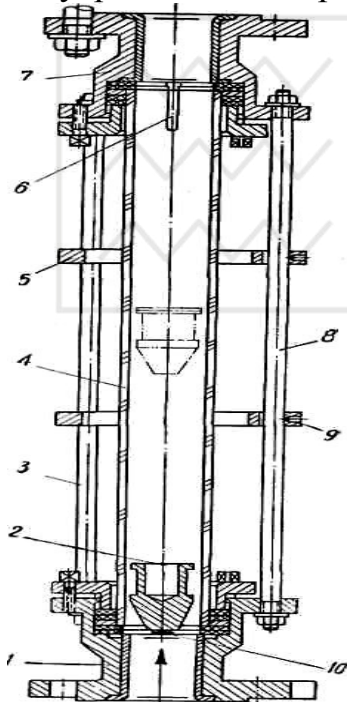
Скляний індикатор витрати типу РС-7:
